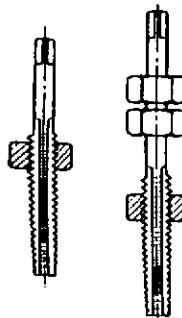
(izquierda). Machos de roscar a máquina (para ser sujeta en una máquina). Fig. 192.5 (derecha). Machos de roscar tuercas (para roscar cortas).
